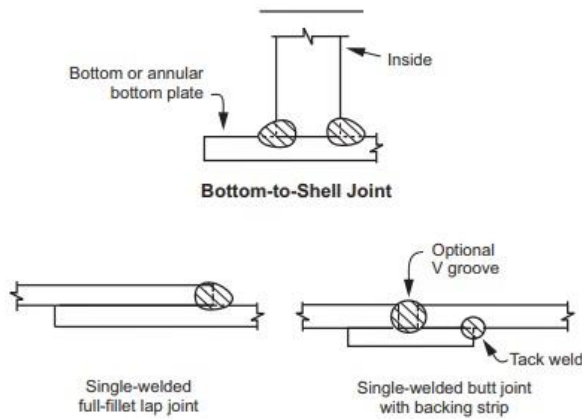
15: Soldaduras horizontales a tope, con traslape. (American Petroleum Institute, 2020)
